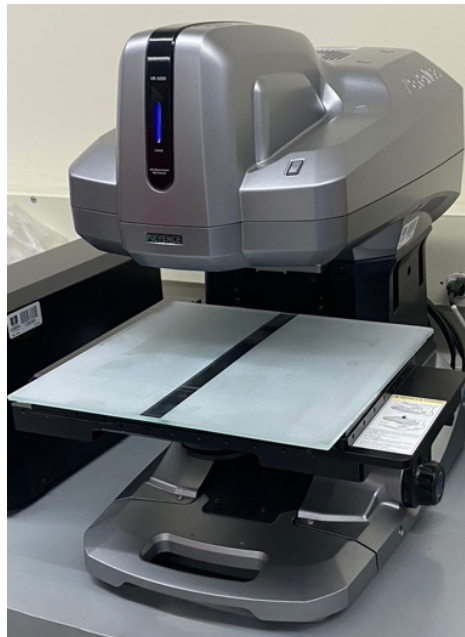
Máquina Keyence durante la prueba de rugosidad.
